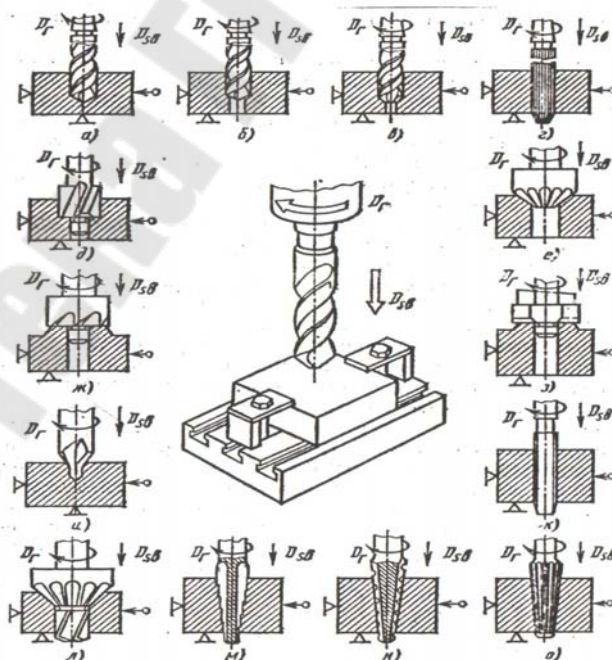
Основные виды обработок, выполняемых на сверлильных станках
